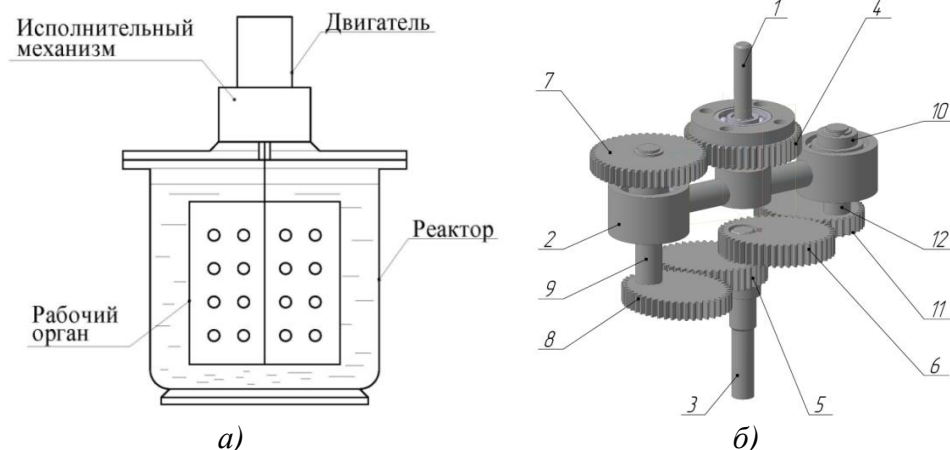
Схема привода перемешивающего устройства (а) и конструкция исполнительного механизма (б):
